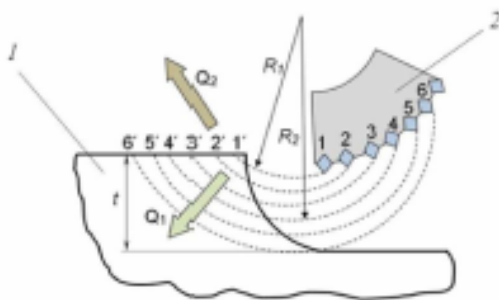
Схема послойного удаления припуска кругом с прерывистой рабочей поверхностью: 1 — заготовка, 2 — сегмент круга
